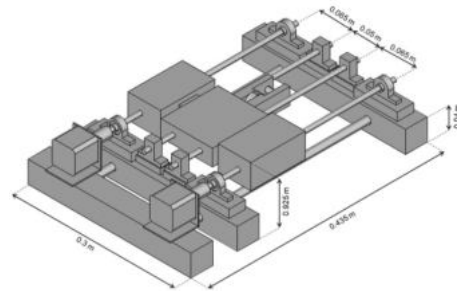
Diseño de la estructura mecánica del proceso de corte.
